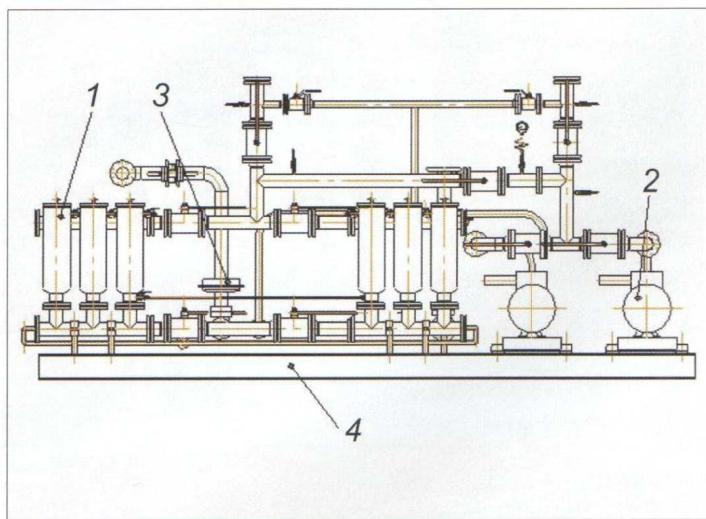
Агрегат смазки АС-1000 для компрессора 66ГЦ-1162/1,3-38 ГТУ:
